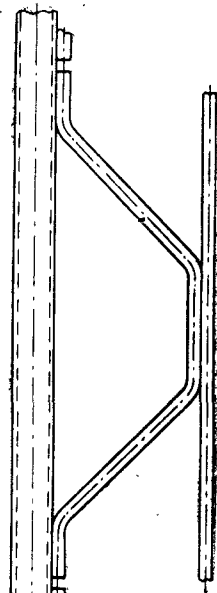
Элемент рамного шпангоута, состоящего из 8-миллиметрового арматурного прутка, сваренного с трубой шпангоута.
